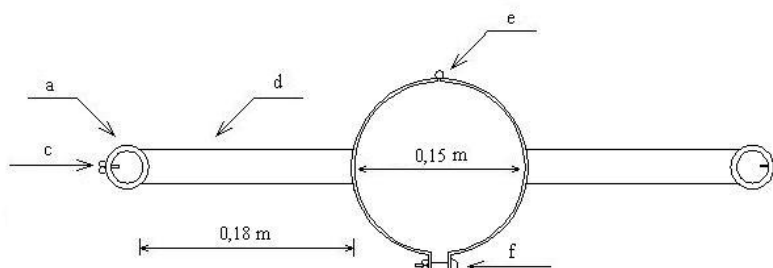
Braçadeira - dimensões e materiais utilizados na confecção da braçadeira.
